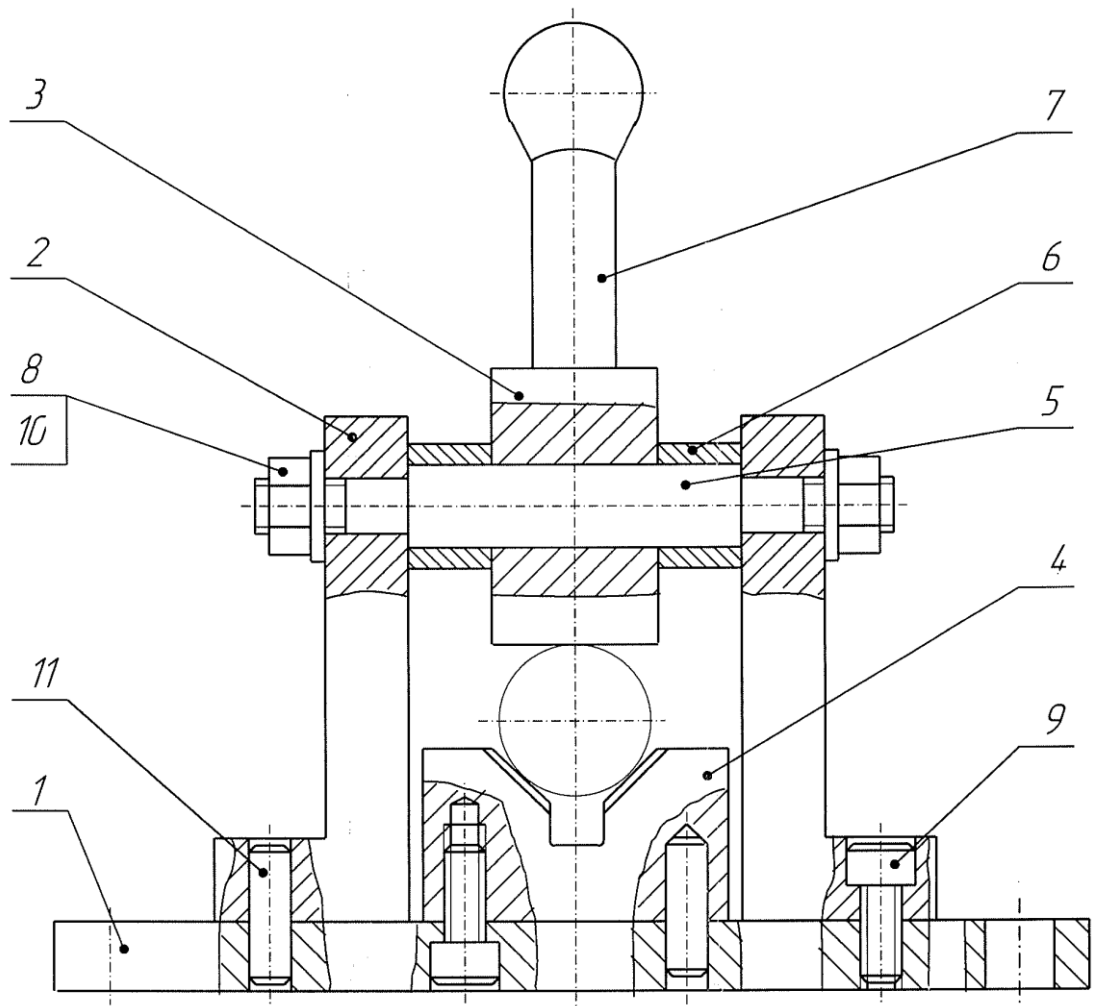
Пристрій за затискання валу: 1 – плита; 2 – стійка; 3 – ексцентрик; 4 – призма; 5 – вісь; 6 – втулка; 7 – ручка; 8 – гайка; 9 – гвинт; 10 – шайба; 11 – штифт
